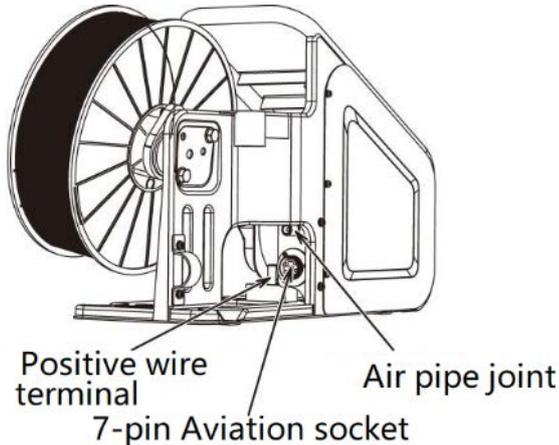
Conexión entre el enchufe de 7 pines de la fuente de potencia de soldadura y la línea de control de 7 pines del alimentador de alambre.
